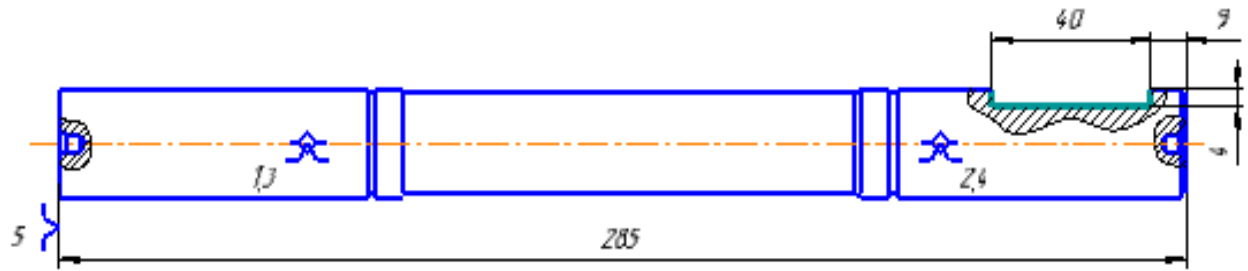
Обробка деталі при шпоночно-фрезерувальній операції.
